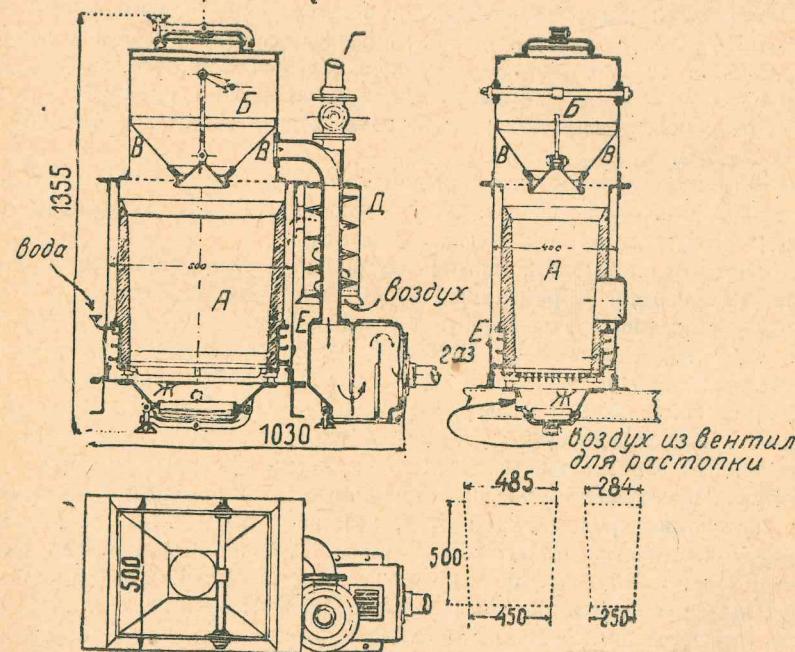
Газогенераторная установка У-1. А — шахта; Б — загрузочная воронка; В — сборник газа; Г — выводная труба для газа при раздувке; Д — подогреватель воздуха; Е — парообразователь; Ж — поддувало
